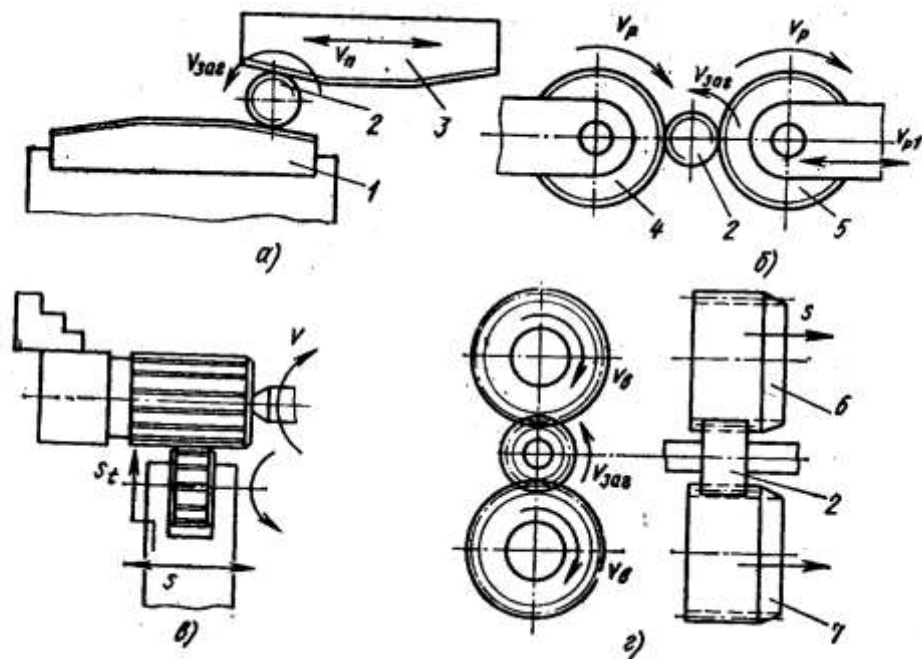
Схеми формуювальних методів обробки пластичним деформуванням
